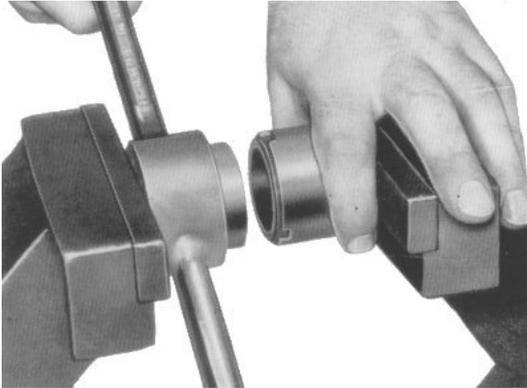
Eindrücken des Dichtringes in den Gewinding mit Hilfe des kombinierten Montageschlüssels
